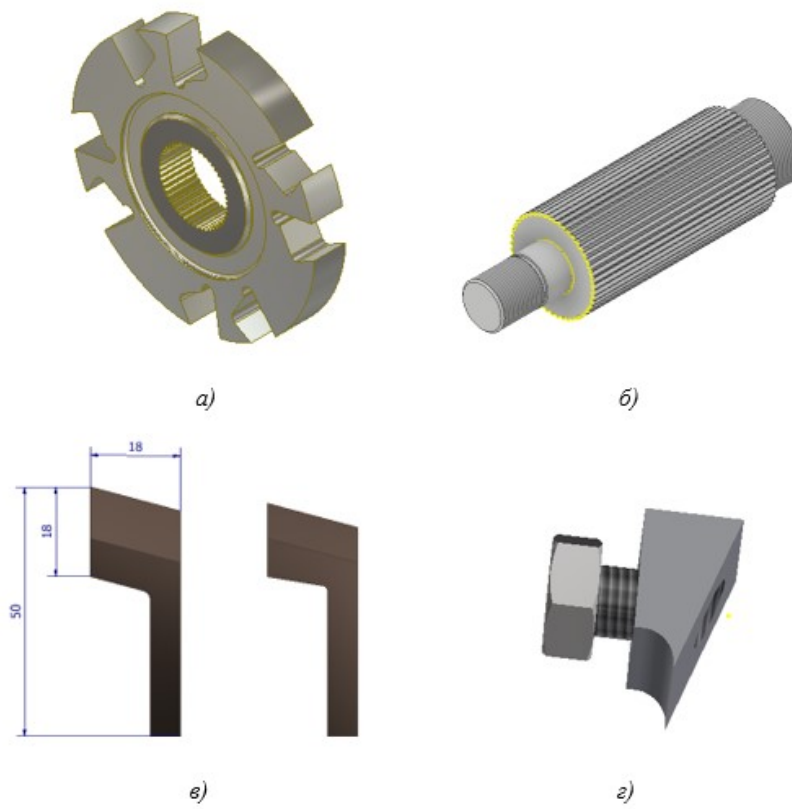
4 - а) корпус фрези, б) шліцевий вал,
